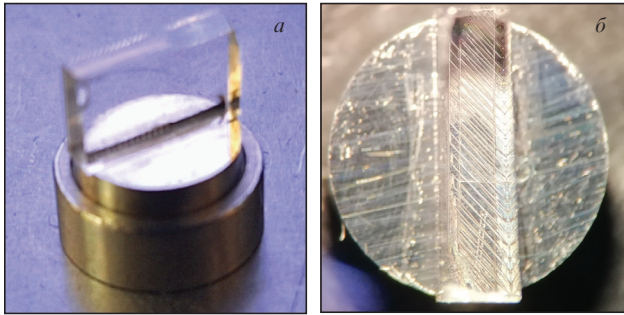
Результат сварки таврового соединения инвар–кварц: общий вид образца (а) и вид сверху (б).
